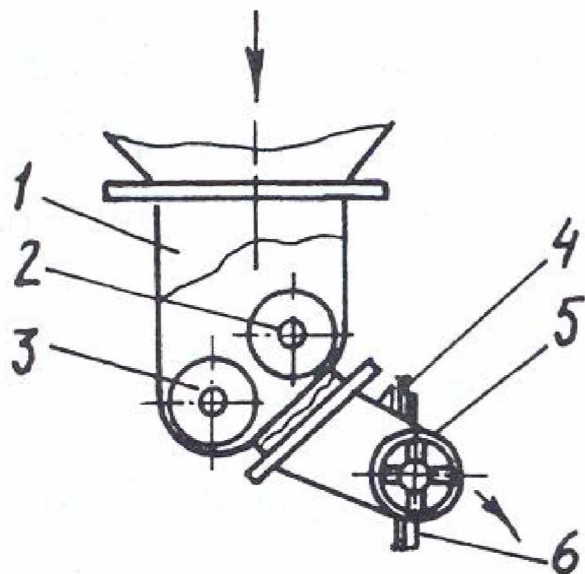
Валковий дозатор: 1 – корпус; 2, 3 – рифлені валки; 4 – заслінка; 5 – маховик; 6 – рейкова передача.
